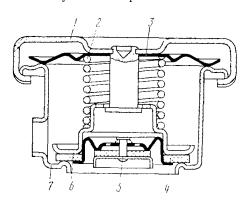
Пробка радиатора: 1 — корпус пробки; 2 — пружина выпускного клапана; 3 — запорная пружина; 4 — прокладка выпускного клапана; 5 —впускной клапан; 6 — выпускной клапан; 7 — горловина радиатора
